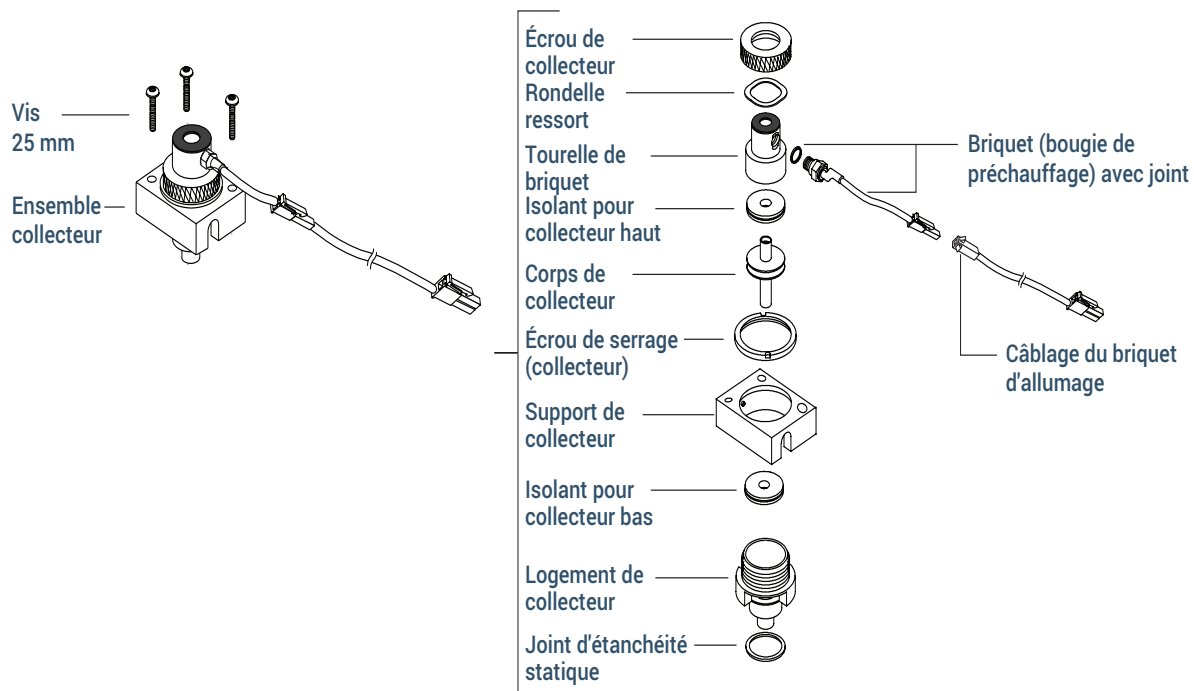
Vue éclatée des pièces pour ensemble collecteur de DIF
